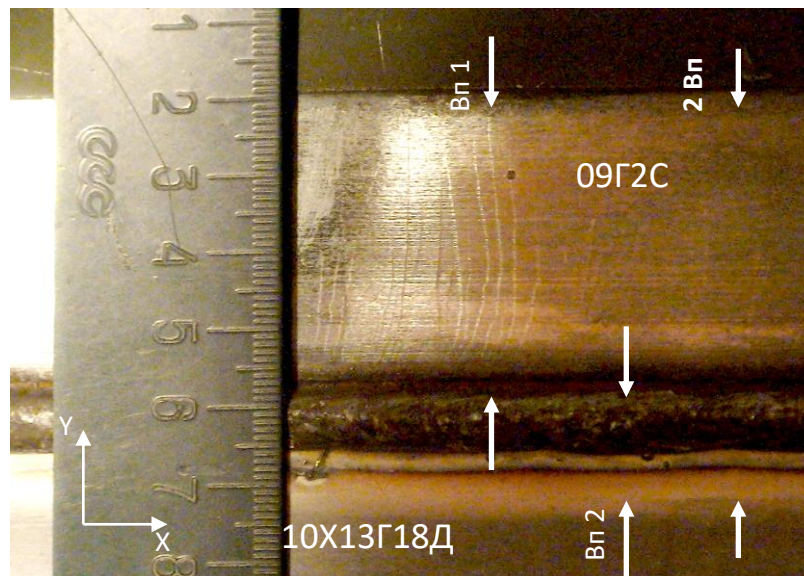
Размеры зон пластической деформации «Вп 1» + «Вп 2» = «2Вп» при сварке сталей 09Г2С+10Х13Г18ДУ
